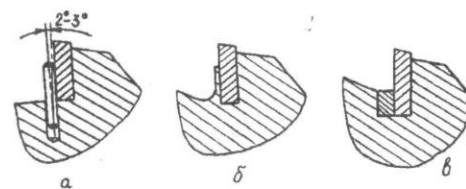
Способы крепления твердосплавных пластинок перед пайкой: а – штифтами; б – технологической стенкой; в – вкладышем из малоуглеродистой стали
